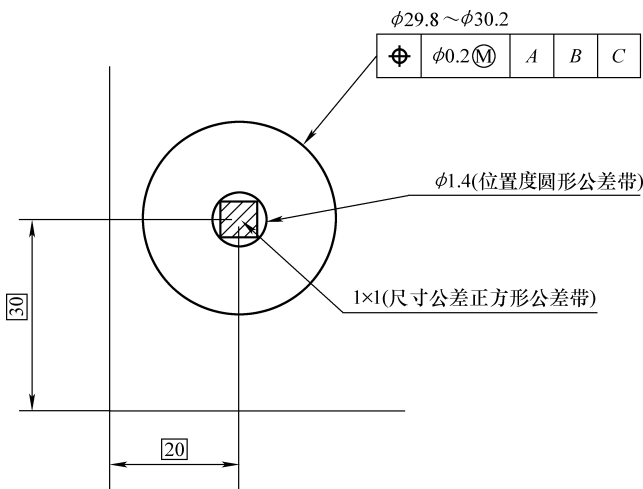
几何公差(位置度)约束的等效公差带
